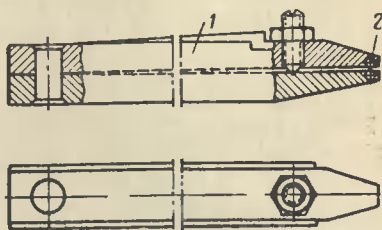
Приспособление для оттяжки уплотнительных колец маслоуловителей.
